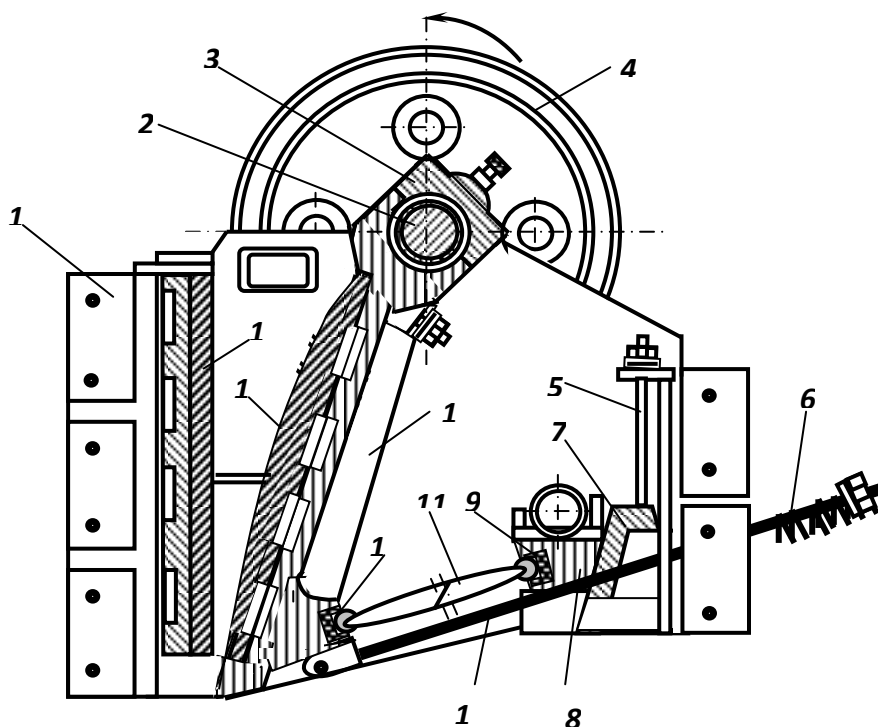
Щековая дробилка со сложным движением щеки типа ЩДС.
